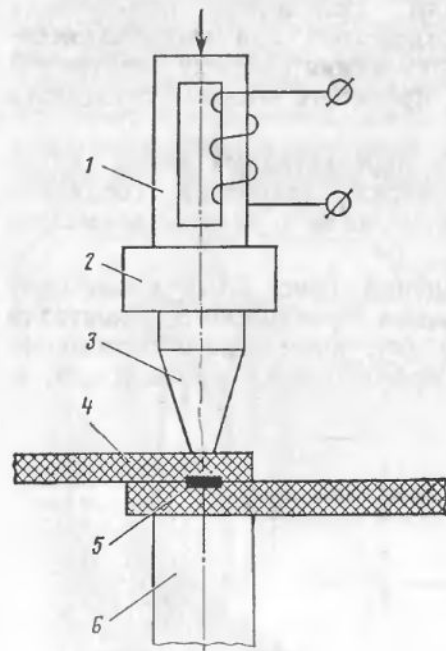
Схема ультразвуковой сварки пластмасс
